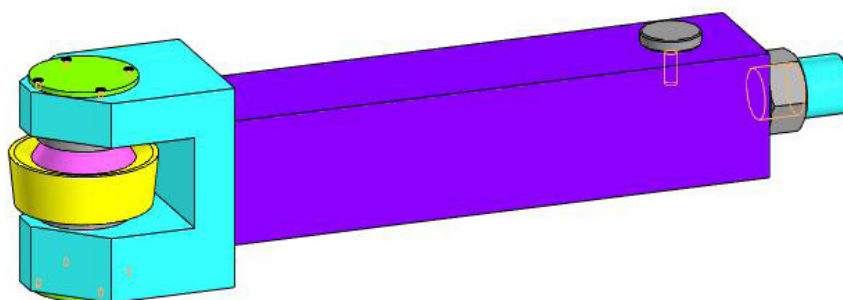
Ротационный поворотный безвершинный токарный резец со стружколомом [2].
